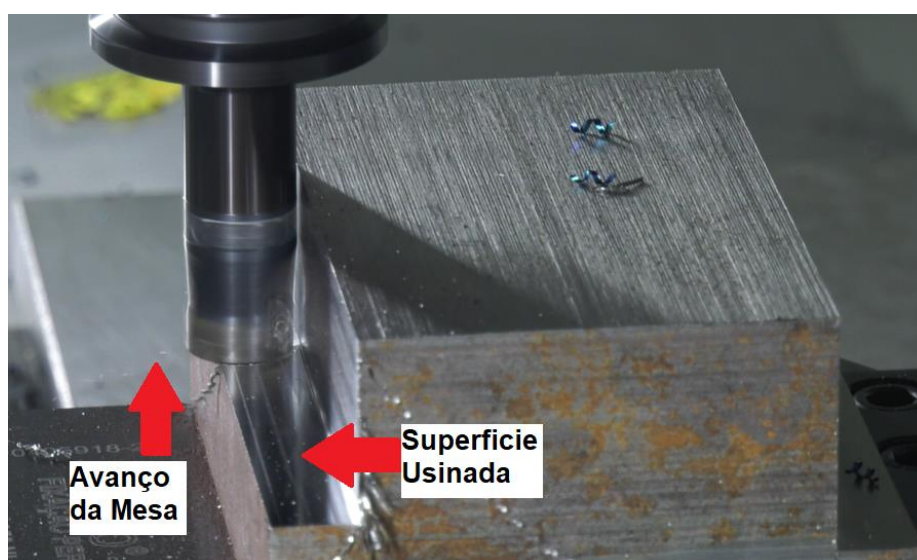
Indicação da superfície usinada e do avanço da mesa, durante fresamento discordante
